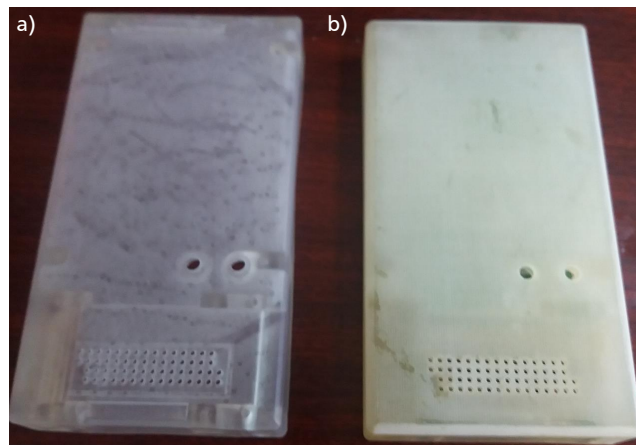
Erprobung additiver Fertigungsverfahren für Gehäuse eines Braille-Demonstrators mit 15 x 4 Pins: a) Mittels STL gedrucktes Gehäuse; b) Mittels Polyjet gedrucktes Gehäuse. Abbildung entnommen aus [299].
